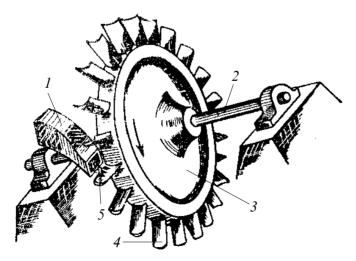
Колесо ротора паровой турбины: I – направляющий аппарат (сопло); 2 – вал; 3 – диск; 4 – рабочая лопатка; 5 – струя пара
